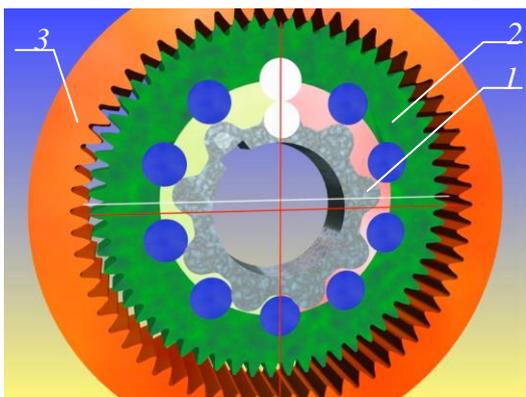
Схема движения вытеснителей в планетарных гидромоторах семейства унифицированных рядов ПРГ-33, ПРГ-22, ПРГ-11, и ПРГ-8: 1 – охватываемый вытеснитель (солнечная шестерня); 2 – охватывающий вытеснитель (сателлит); 3 – корпус (коронная шестерня)
